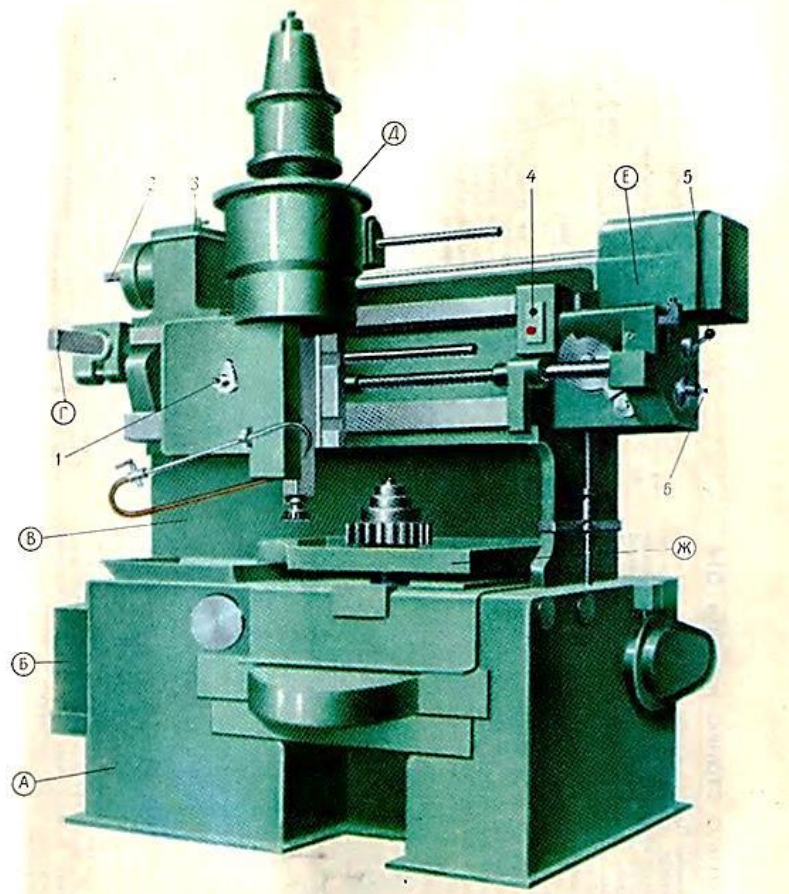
Загальний вид базової моделі верстата 514
